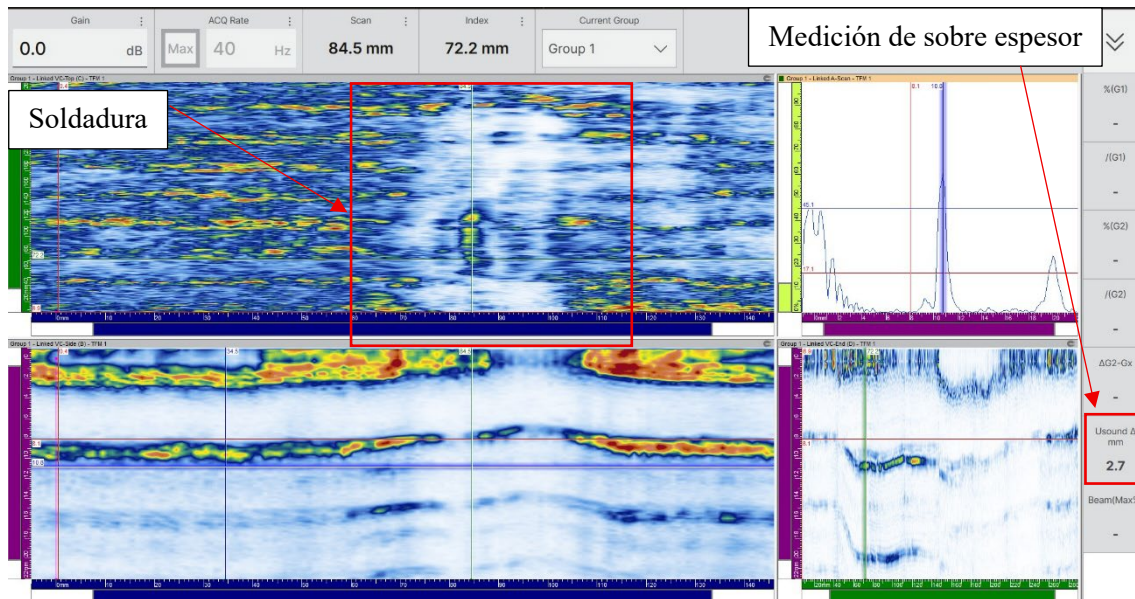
Escaneo en la zona de la soldadura. Medición de sobre-espesor.
